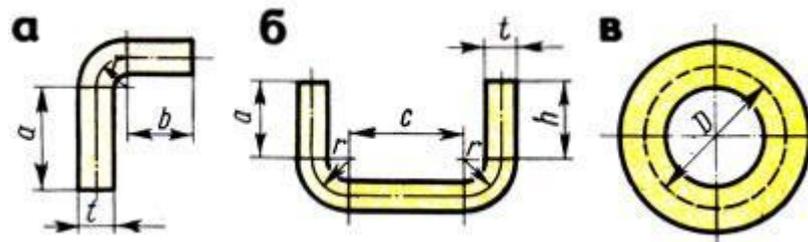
Схемы для определения длины заготовок: а - угольника с внутренним закруглением, б - скобы с закруглением, в - кольца
